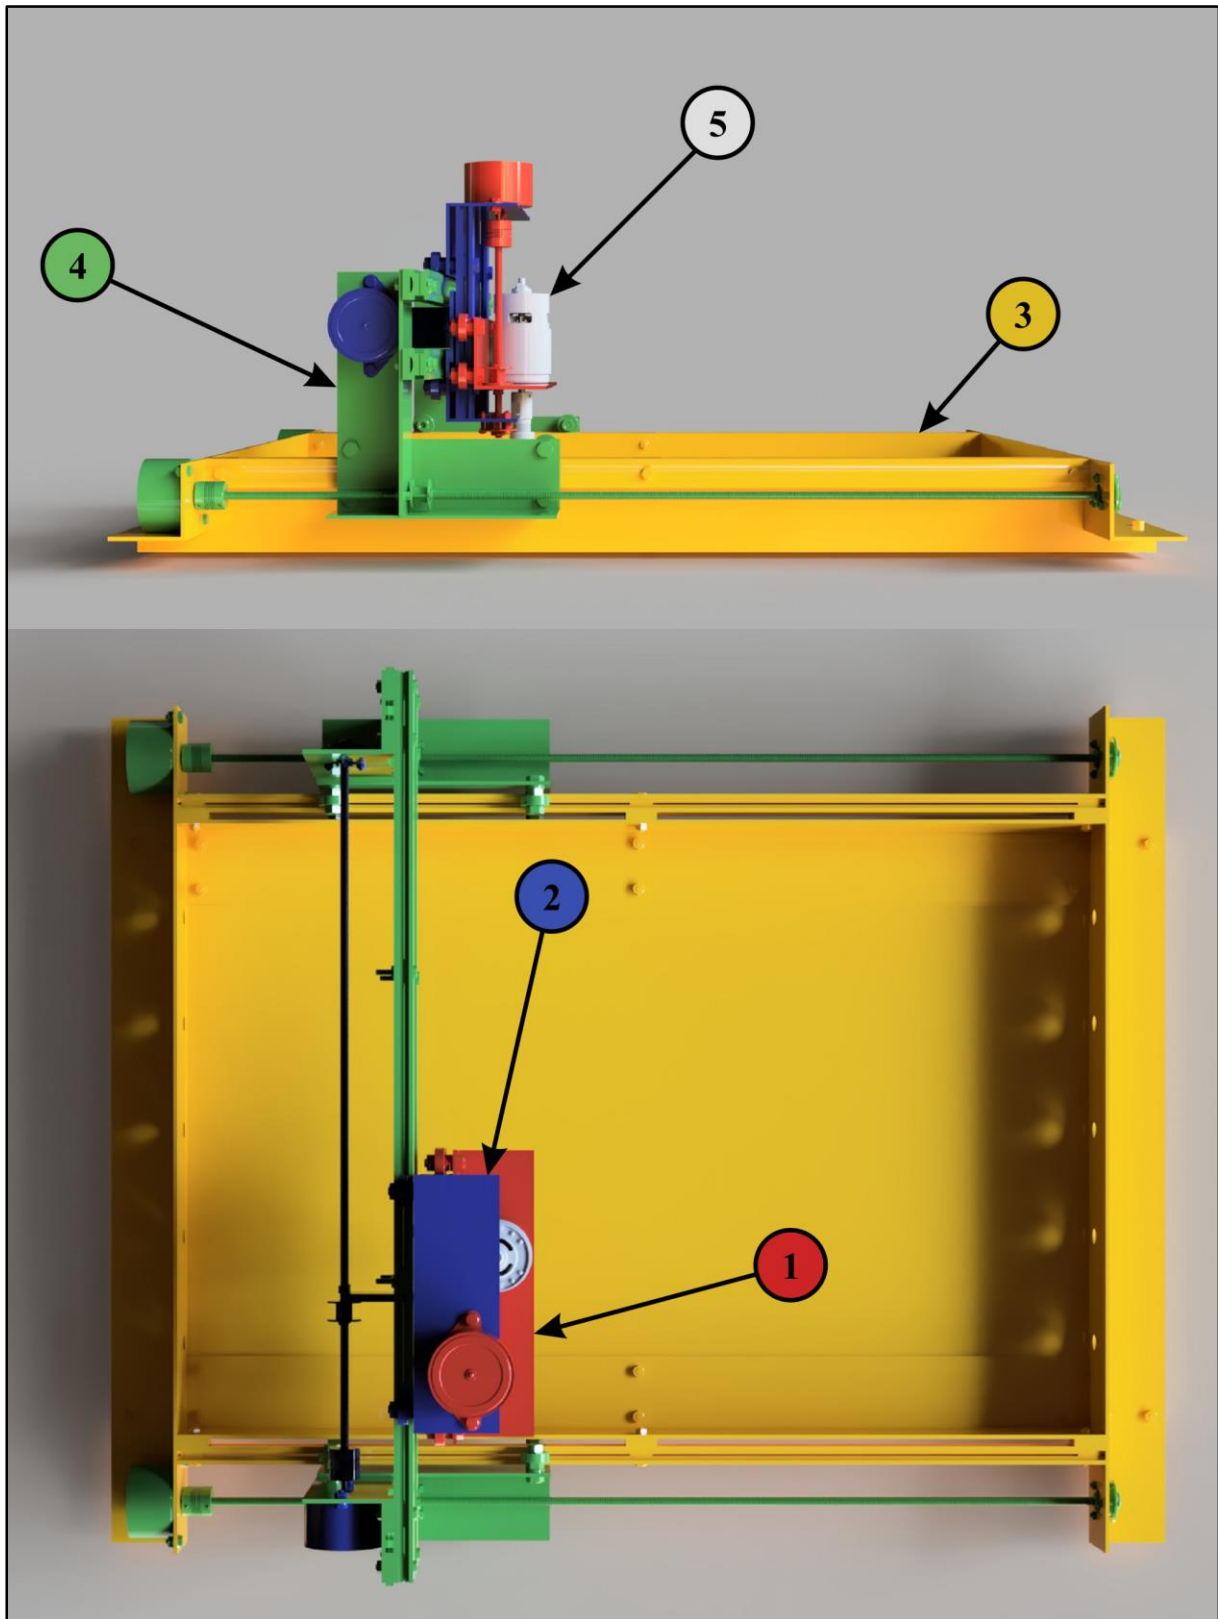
Les composants de base d'une machine CNC à 3 axes.
